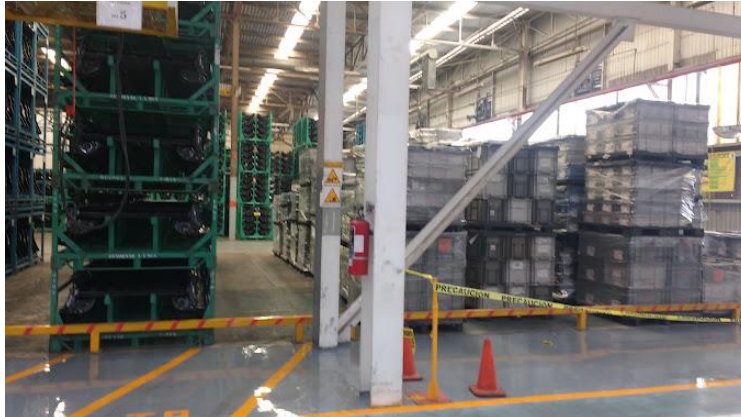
3 Interior de la planta Fuente: YMEX 2024
